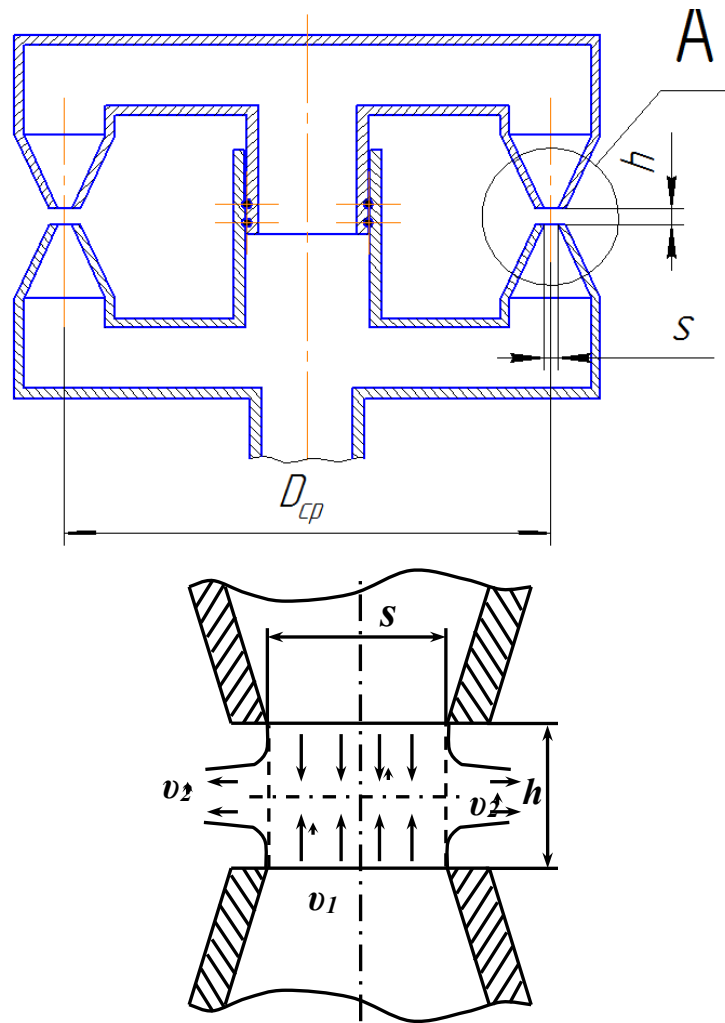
Схема протиточно-струминної головки гомогенізатора: а – загальний переріз, б – вид А перерізу.
